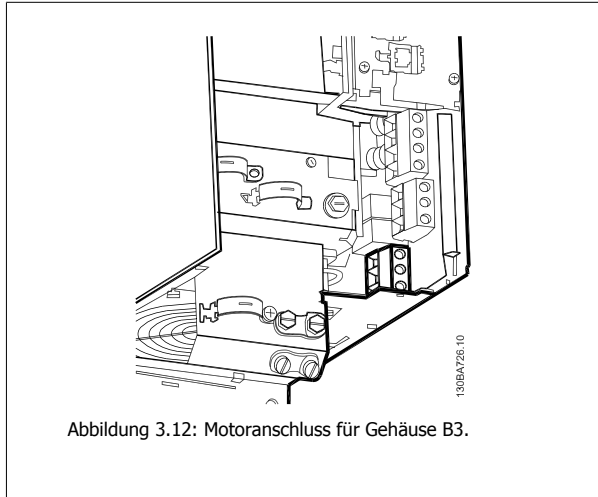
Motoranschluss für Gehäuse B3.
